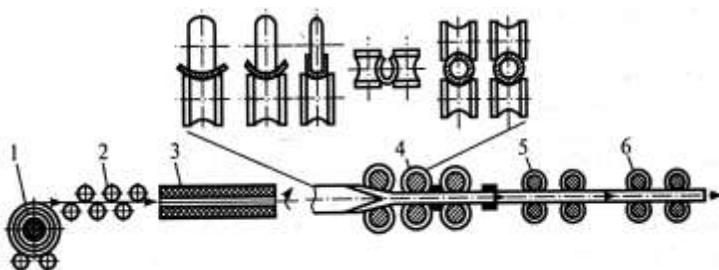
Схема производства труб непрерывной печной сваркой: 1 – штрипс в рулонах; 2 – тянущие ролики; 3 – нагревательная печь; 4 – формовочно-сварочный стан; 5 – клетки редукционного стана; 6 – клетки калибровочного стана
